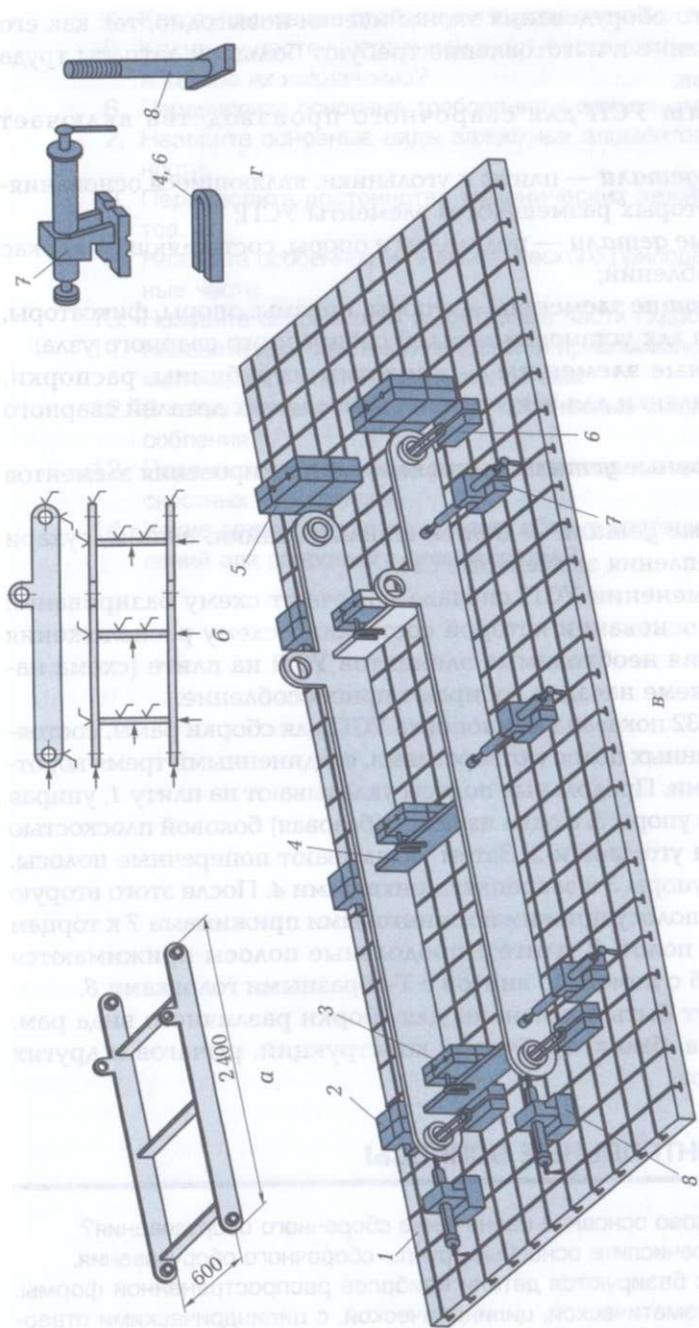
Компонетка универсально-сборного приспособления для сборки рамы: 1 — плита; а — изделие; б — схема базирования; в — компоновка с изделием; г — элементы универсально-сборного приспособления: 1 — плита; 2 — угольники; 3 и 5 — упоры; 4 и 6 — прихваты; 7 — винтовые прижимы; 8 — Т-образная головка
